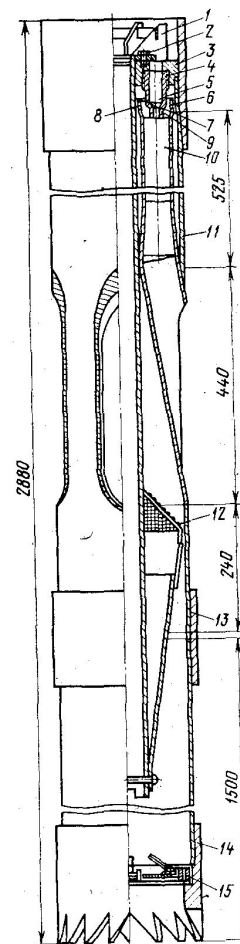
Металлоулавливатель Р. С. Яремейчука и Э. И. Узумова:
